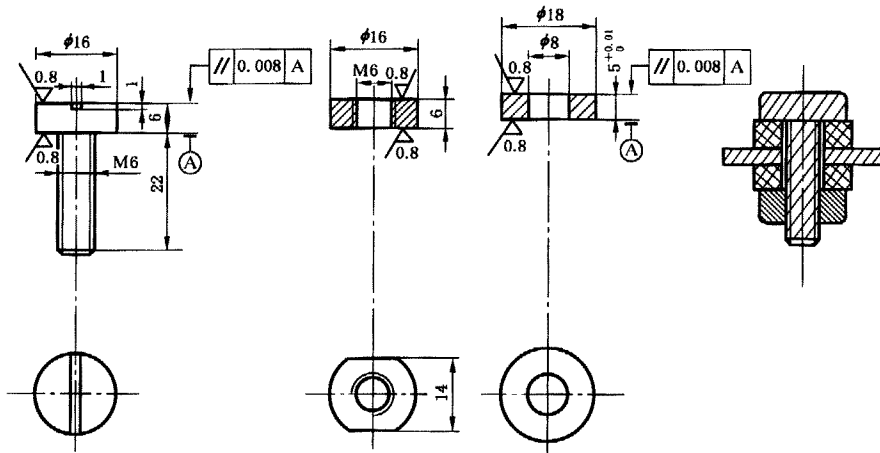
螺钉、螺母缝隙结构的零件及装配图
